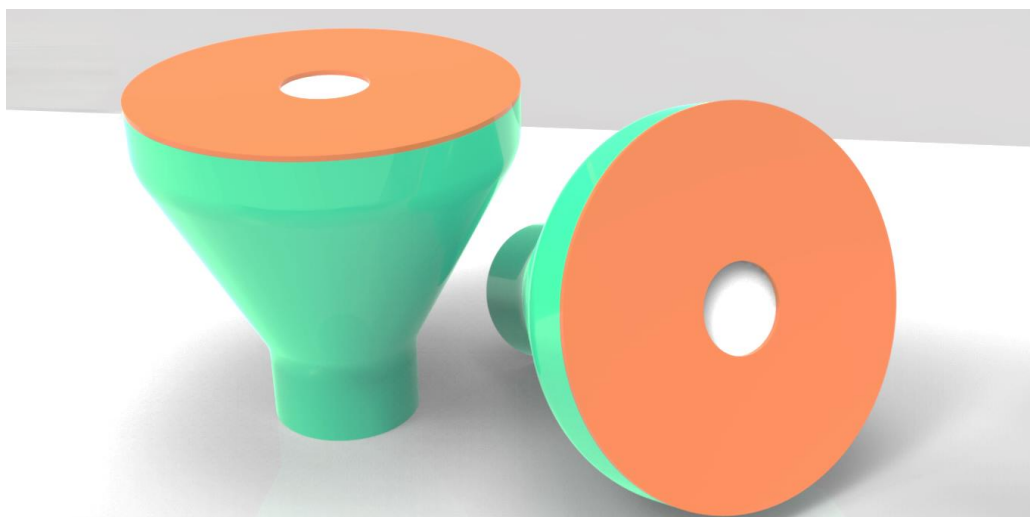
Montagem explodida e materiais da cápsula sanitizante
